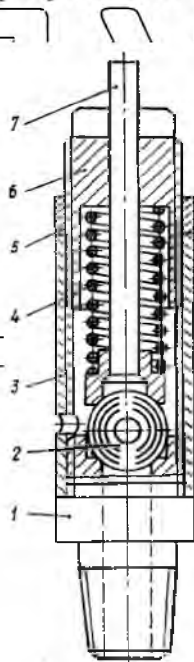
10. Запобіжний клапан; 1 - сідло клапана; 2 - кульковий клапан; 3 - корпус; 4 - пружина; 5 - контргайка; 6 - регулювальний гвинт; 7 - стрижень клапана.
